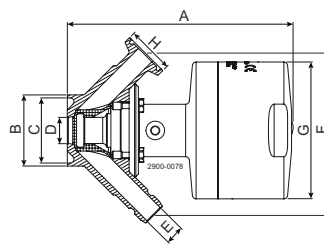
Pneumatisch mit Ventilgehäuse: Rohr mit Kragen Schweißen
